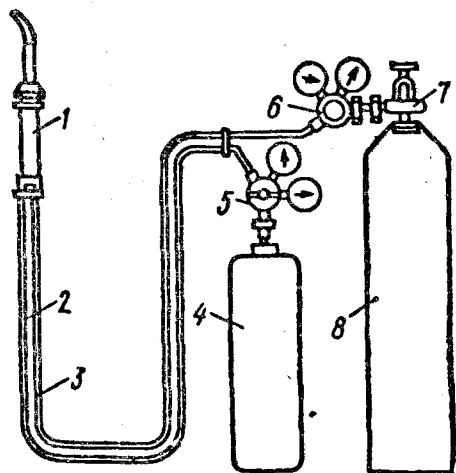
Оборудование поста для газовой сварки: 1 — горелка; 2 — шланг для подвода ацетилена; 3 — шланг для подвода кислорода; 4 — ацетиленовый баллон; 5 — ацетиленовый редуктор; 6 — кислородный редуктор; 7 — кислородный вентиль; 8 — кислородный баллон
